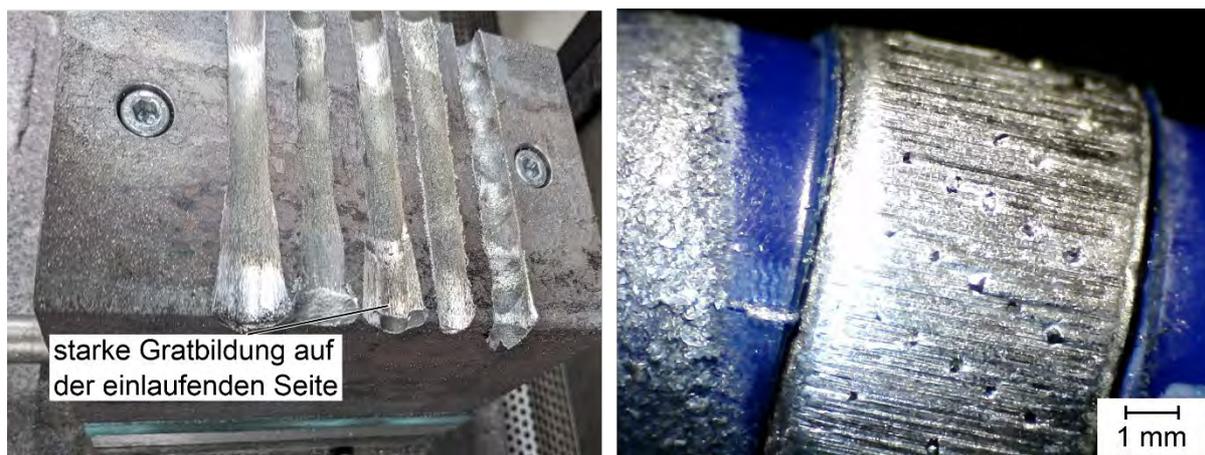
Versuchsaufbau in der Schleifmaschine und Bilder der Prototypen-Werkzeuge mit deterministischem Muster
